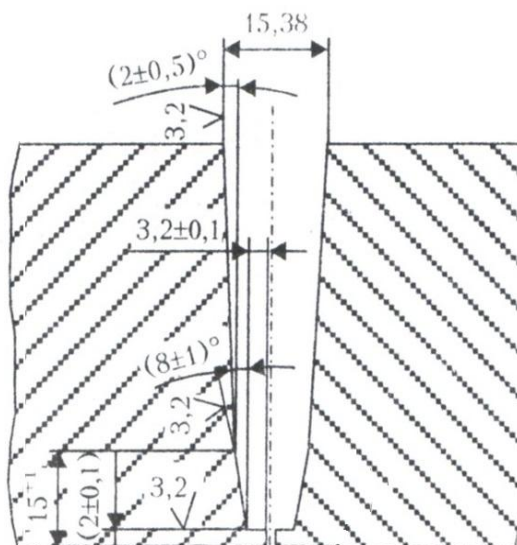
Схема U-образной разделки для сварки в УЩР
